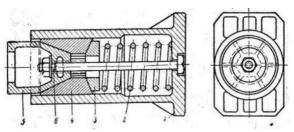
Фрикционный буфер с разрезным коническим кольцом 1 - корпус, 2 - пружина, 3 - упорная шайба, 4 - сегмент разрезного конического кольца, 5 - упор, 6 - болт.
